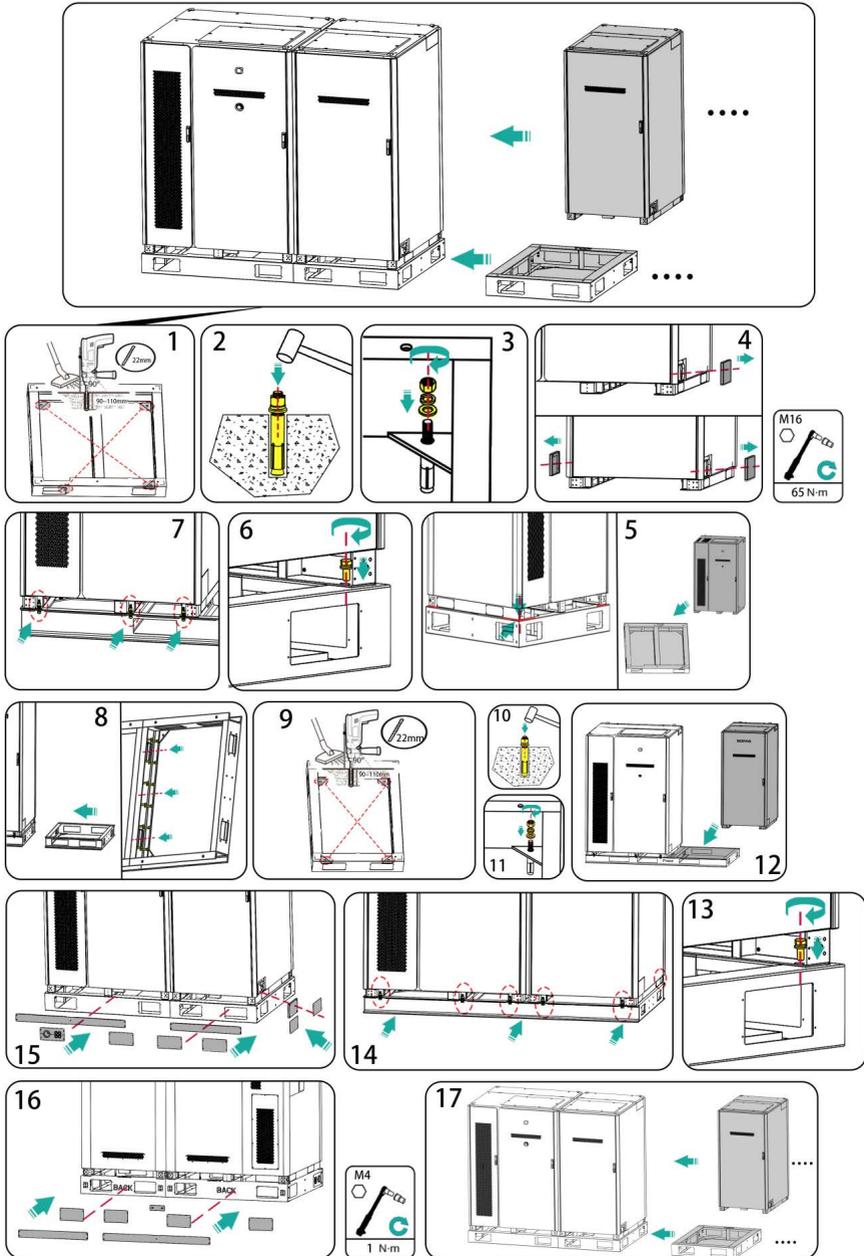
Installationsschema der Lösung mit Stahlsockel
